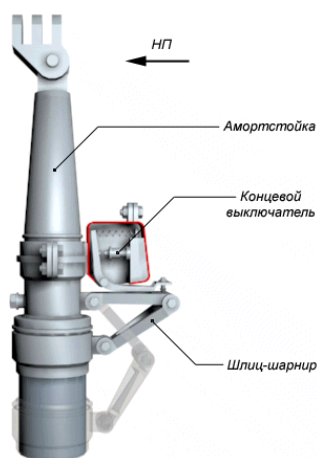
Расположение шлиц-шарнира и концевого выключателя
